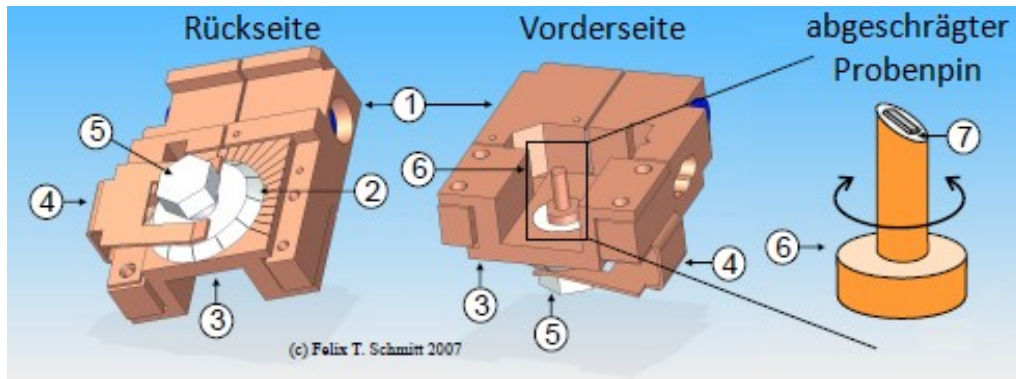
1) Transferierbarer Teil des Probenhalters. 2) Aluminiumschraube für azimutale Probenrotation. 3) Winkelskala 4) Haltefedern. 5) Sechskant-Schraubkopf zum Einstellen der Rotation. 6) Probenpin. 7) Probe. Nach [35]
